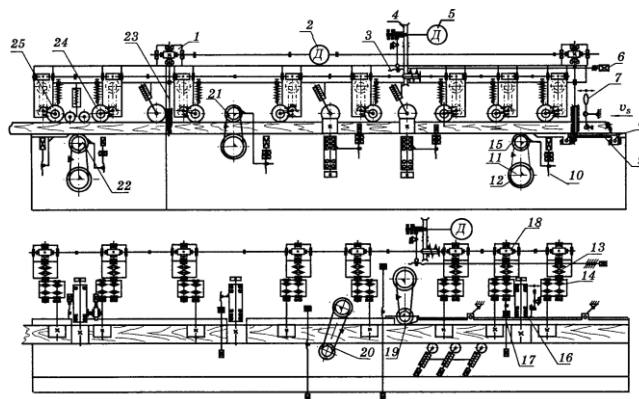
Кінематична схема чотирибичного верстата: 1 — черв'ячні передачі; 2, 5, 12 — електродвигуни; 3 — гвинтова пара; 4 — клинопасовий варіатор; 6, 7 — ручки; 8 — важільний механізм регулювання; 9 — передній стіл; 10, 17 — гвинтові пари; 11 — клинопасова передача; 13, 14 — спарені ланцюгові передачі; 15 — нижній горизонтальний шпindel; 16 — підшипникові опори; 18 — черв'ячні редуктори; 19 — правий вертикальний шпindel; 20 — лівий вертикальний шпindel; 21 — верхній горизонтальний шпindel; 22 — додатковий горизонтальний шпindel; 23 — гвинтові пари; 24 — подавальні вальці; 25 — гладкий валець
